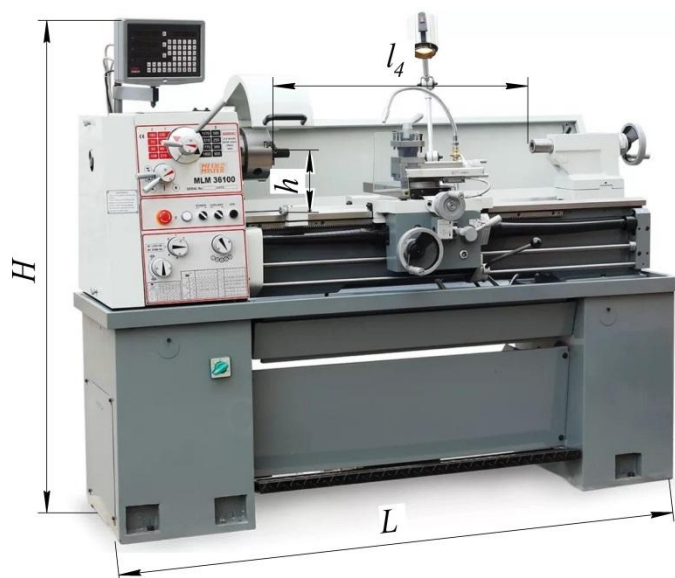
Токарный станок; расстояние между центрами и габаритные размеры
